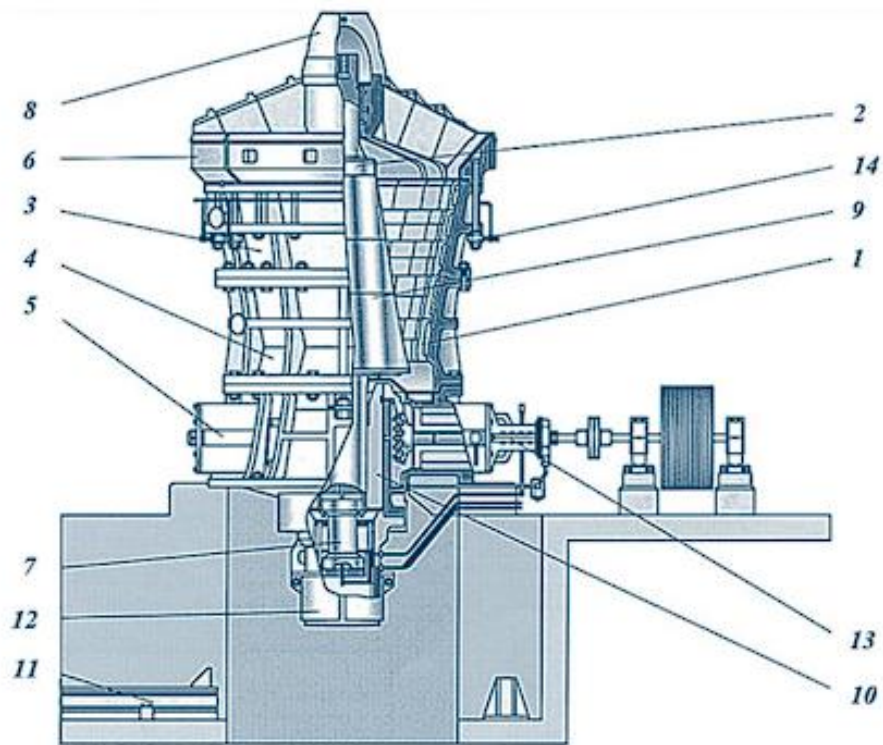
Складові елементи конусної дробарки типу ККД з гідравлічним регулюванням вихідної щілини: 1 – нерухома конічна чаша; 2 – дробильний конус; 3, 4, 5 – верхнє, середнє і нижнє кільця станини; 6 – траверса; 7 – головний вал; 8 – захисний ковпак; 9 – броня (футерування) рухомого конуса; 10 – ексцентриковий стакан; 11 – рейкова колія; 12 – плунжер; 13 – привод дробарки; 14 – гідравлічний домкрат
